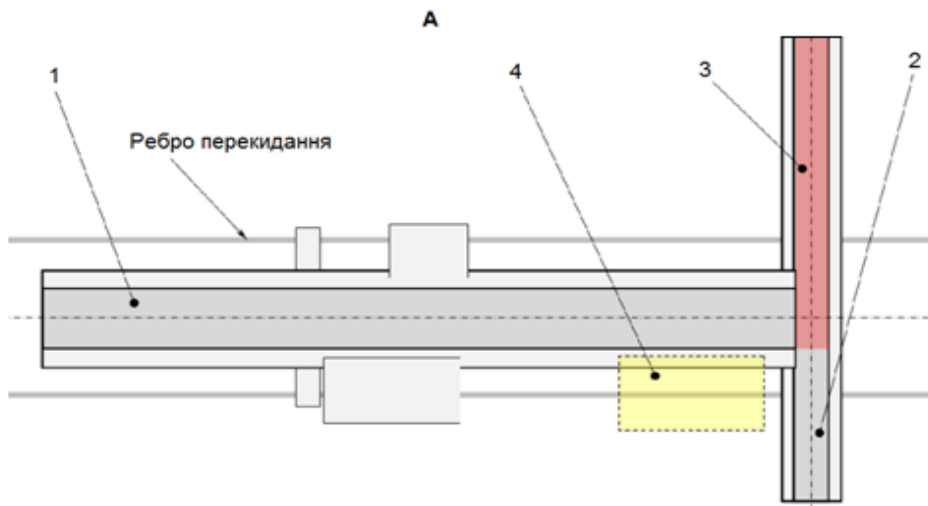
Розрахункова схема щодо стійкості штабелеукладача на перекидання в плані
